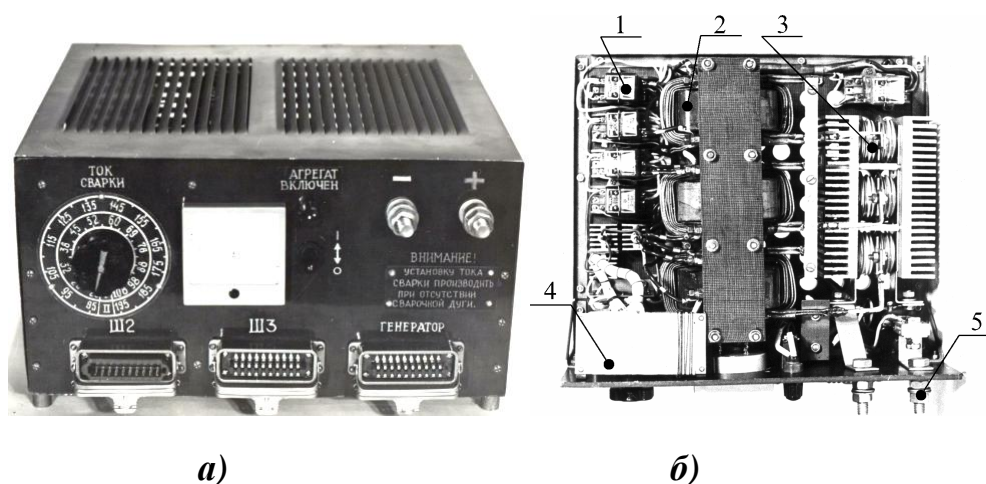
Внешний вид сварочного блока *а*), блок управления без кожуха *б*), 1 – реле; 2 – согласующие трансформаторы; 3 – силовой выпрямитель; 4 – дешифратор; 5 – выводы для подключения сварочных проводов
